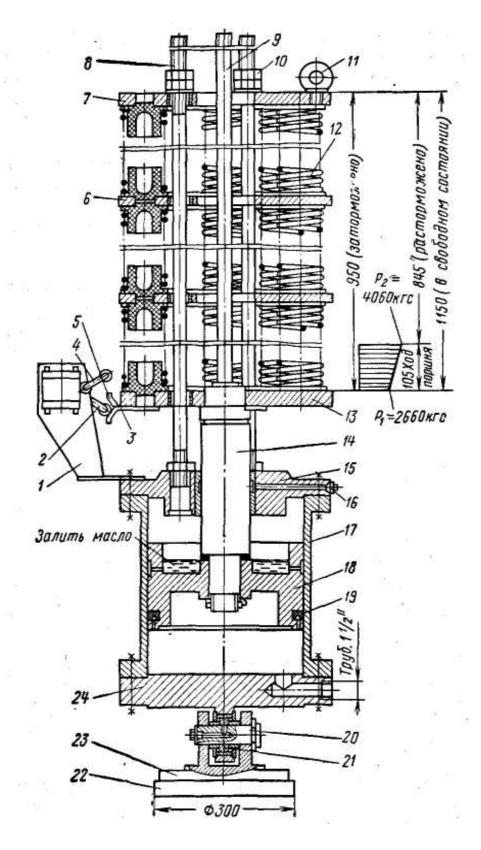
Пружинно-пневматический безгрузовой привод тормоза
